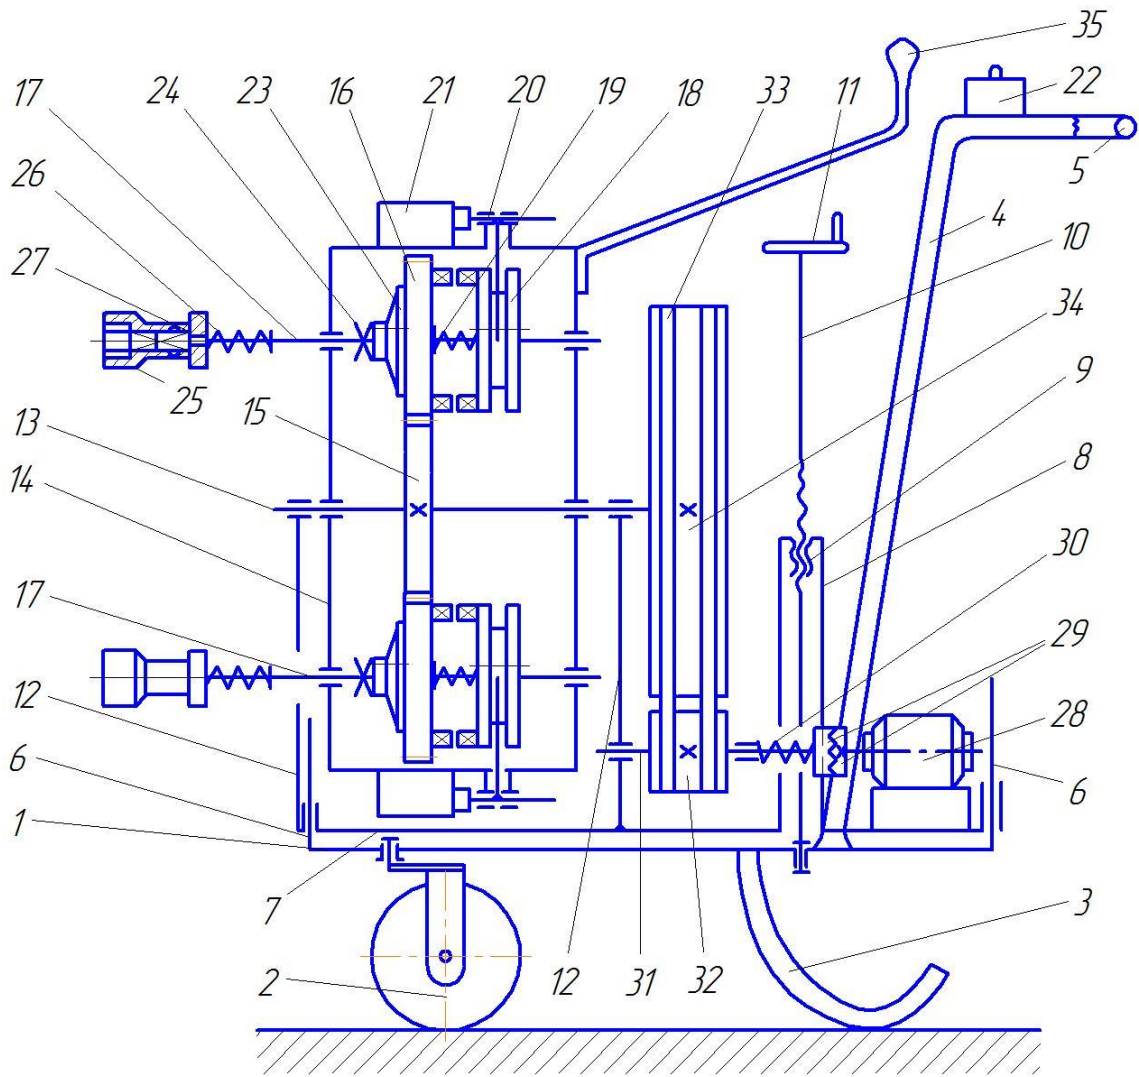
Конструктивна схема електромеханічного багатшпindelного гайкокрута для гайок коліс автомобілів.
